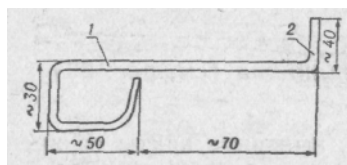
Крючок-извлекатель пуль для пневматической винтовки «312» (ГДР)
